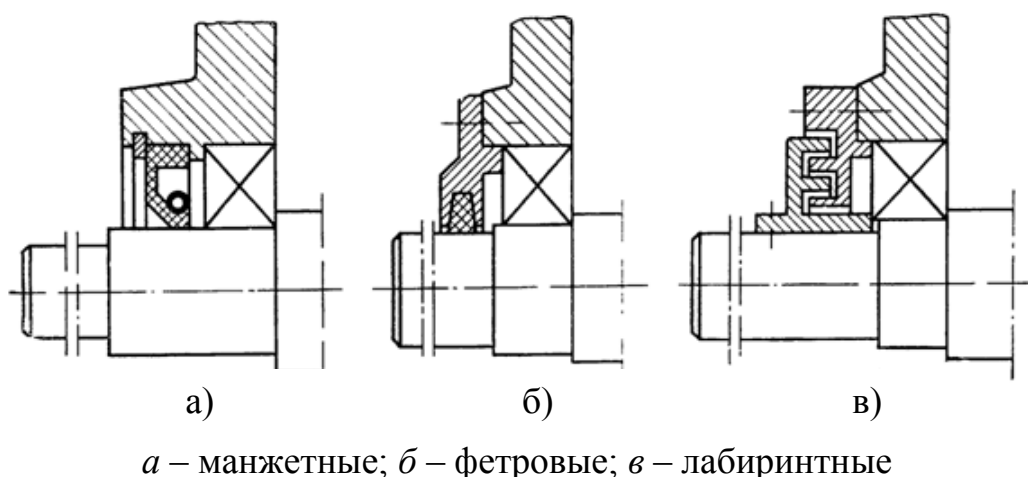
Виды уплотнений подшипниковых узлов
